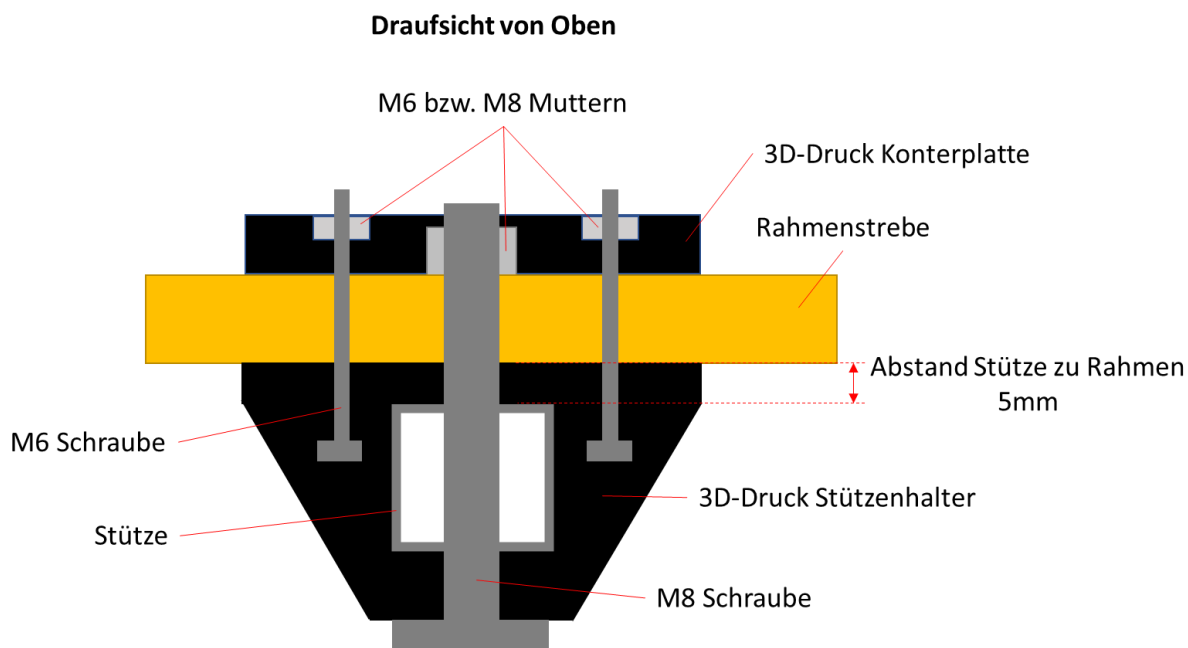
Prinzipskizze der Stützenhalter, Draufsicht von oben, nicht maßstabsgetreu
